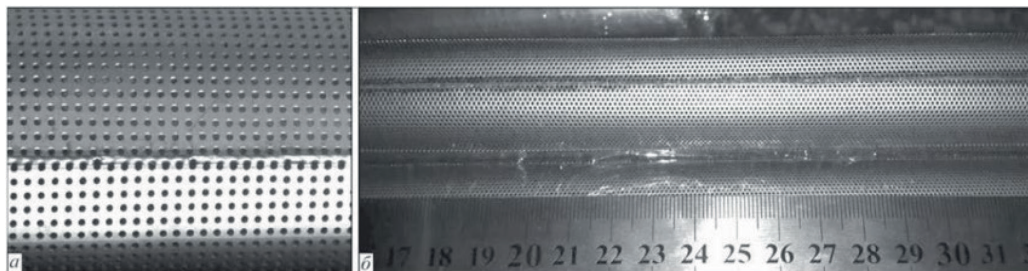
Зовнішній вигляд зварного з'єднання (а) та зразка (б) фільтруючого елемента з нержавіючої сталі 08X18H10T ($\delta = 0,5$ мм), отриманого лазерним зварюванням з порошковою присадкою ПГ-10Н-04²⁷
